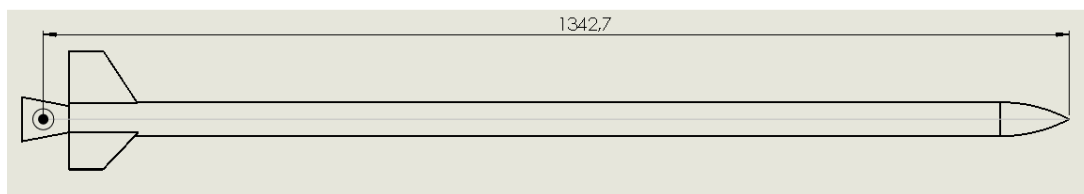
CP de la parte externa del motor representado en el cuerpo
